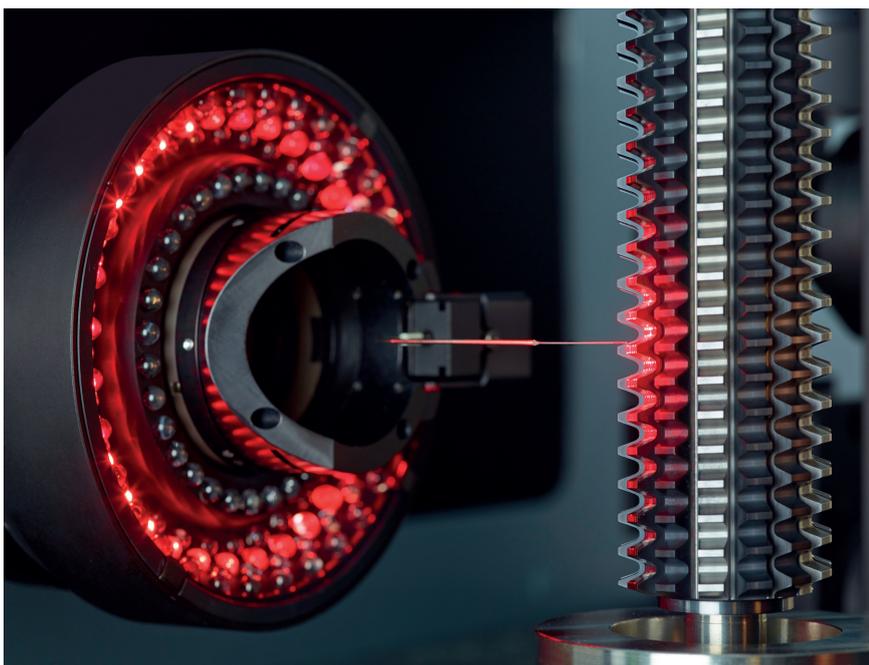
Mikrowälzfräser mit Modul von weniger als 0,05 mm © Werth
